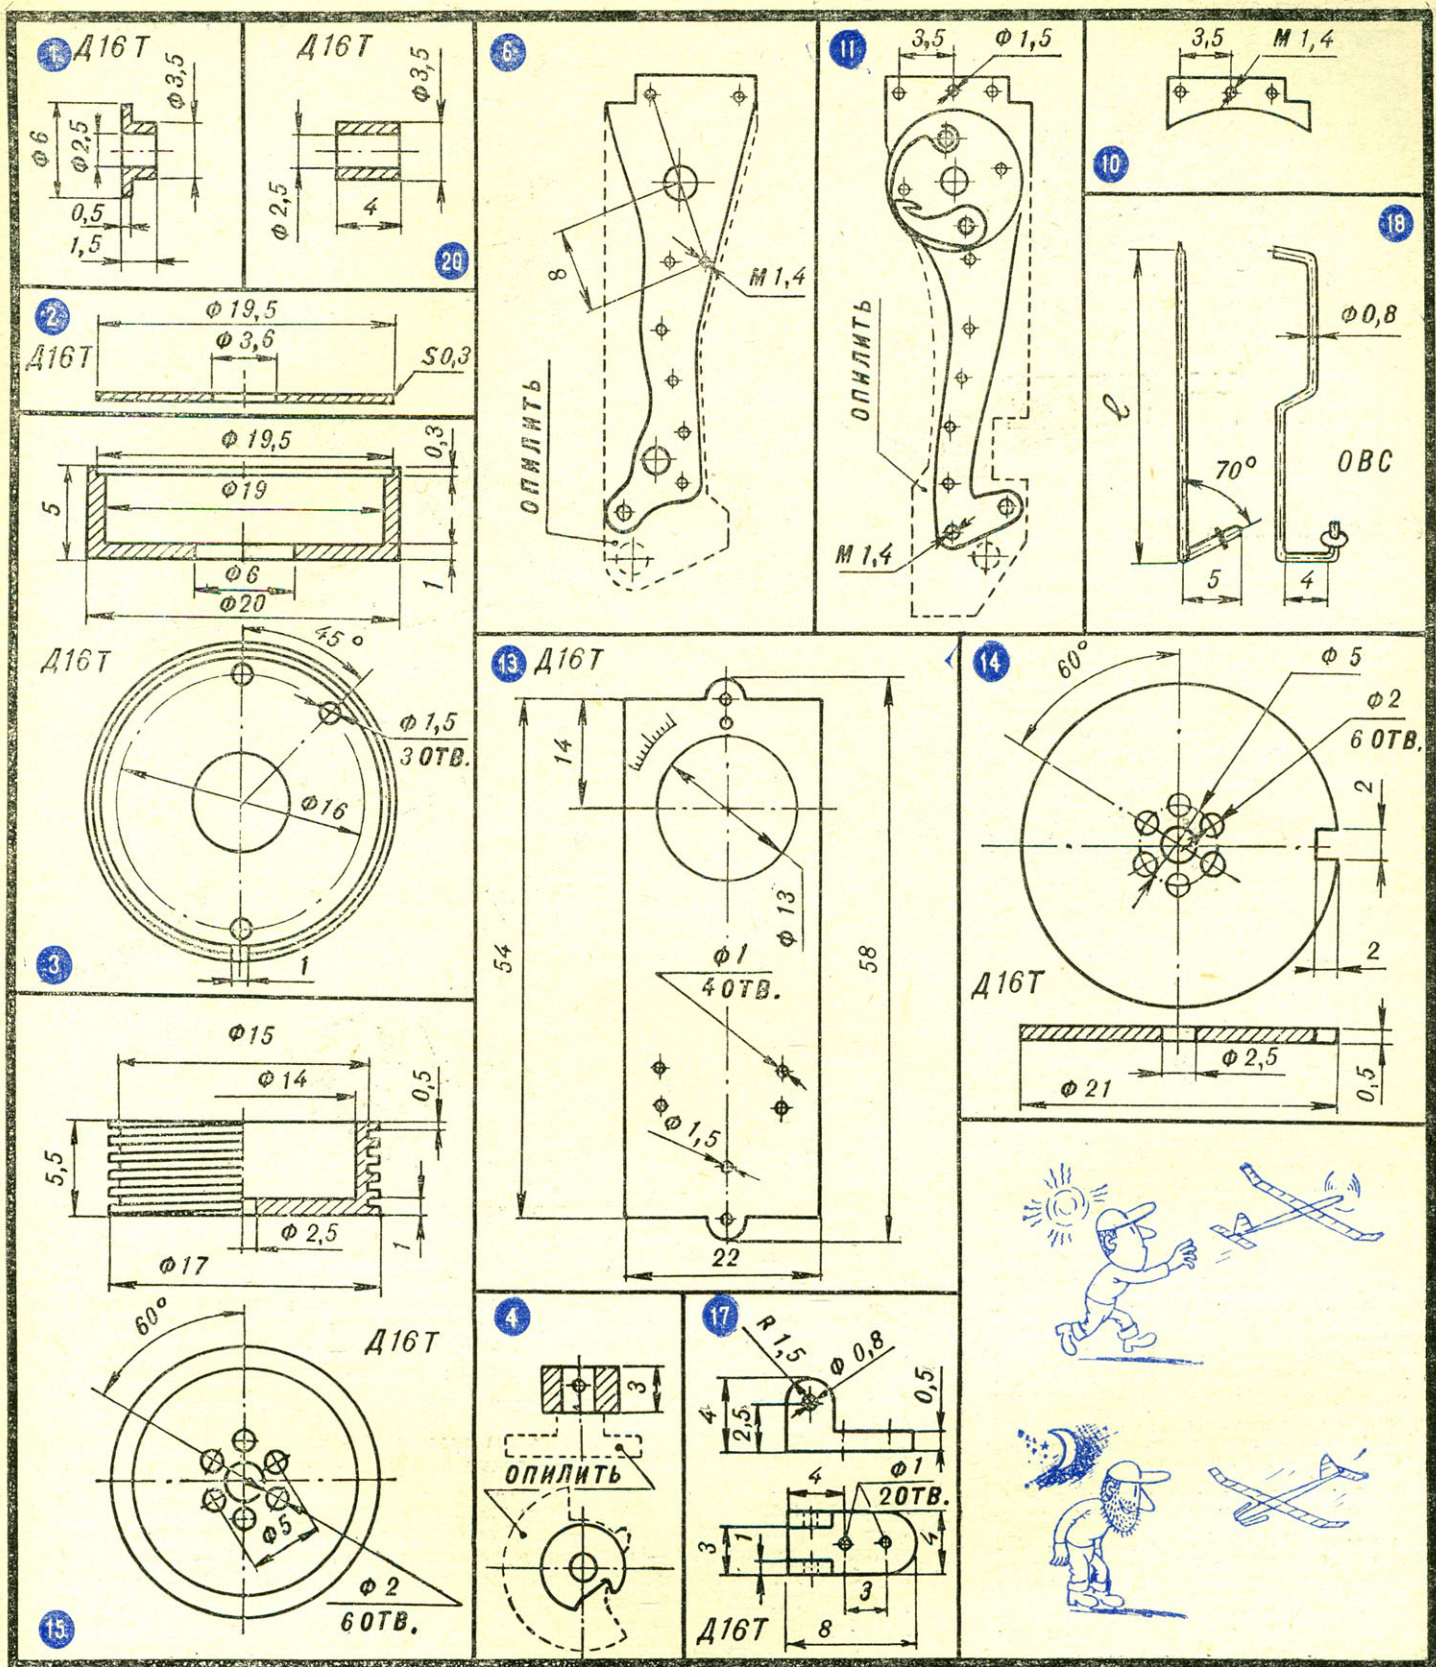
Устройство таймера резиномоторной модели: 1 — прижимная шайба, 2 — крышка корпуса, 3 — корпус, 4 — фиксатор пружины, 5 — штифт, 6, 11, 13 — платы, 7 — шестерни, 8 — анкер, 9 — распорная втулка, 10 — сухарик, 12 — вал, 14 — диск программного механизма на руль направления, 15 — барабан, 16 — пружина, 17 — кронштейн, 18 — рычаг, 19 — заклепки, 20 — втулка.
